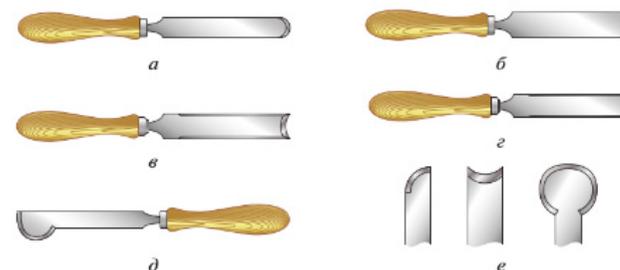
Виды резцов-стамесок: а — полукруглая; б — косая; в — для валиков; г — плоская прямоугольная; д — резец-крючок; е — фасонные
